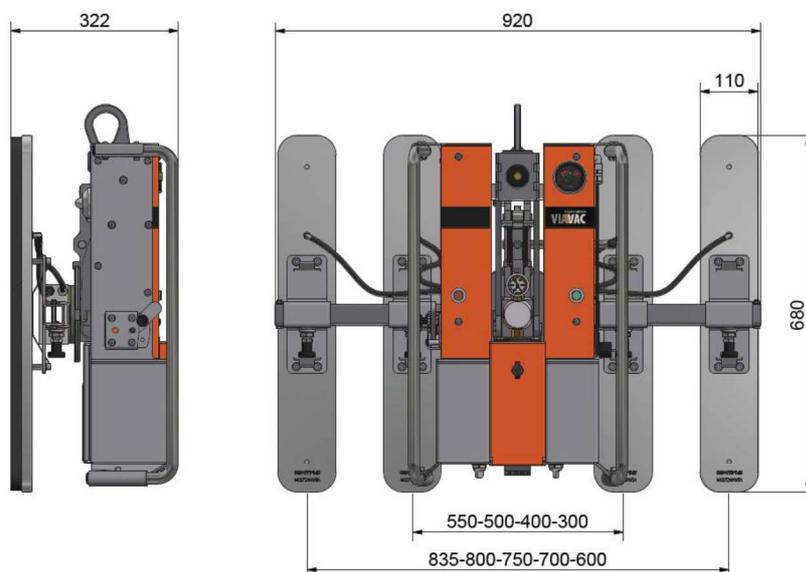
Dimensions Cladboy compact Flex CBC3 en mm
